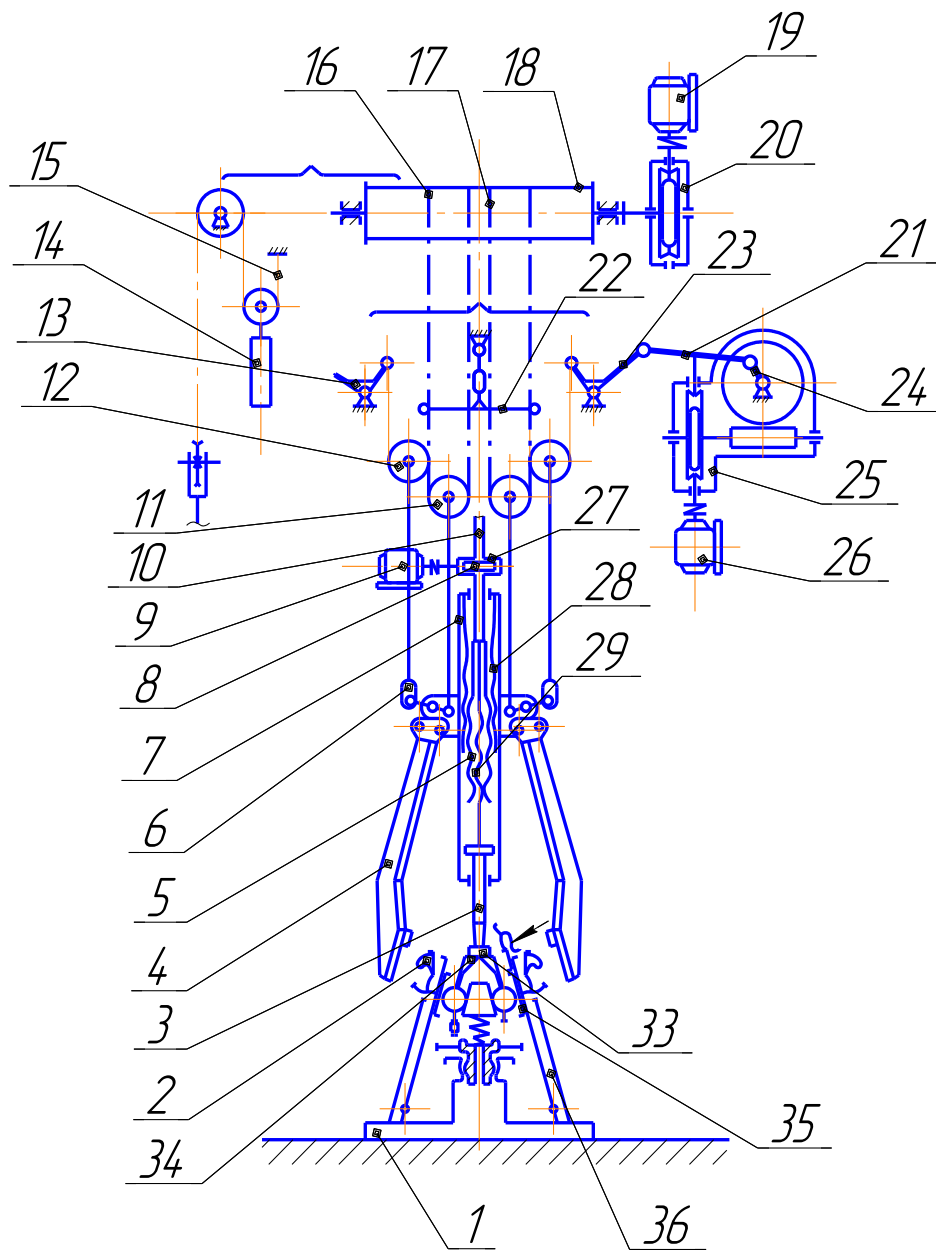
Кінематична схема механізму стріперного пристрою
